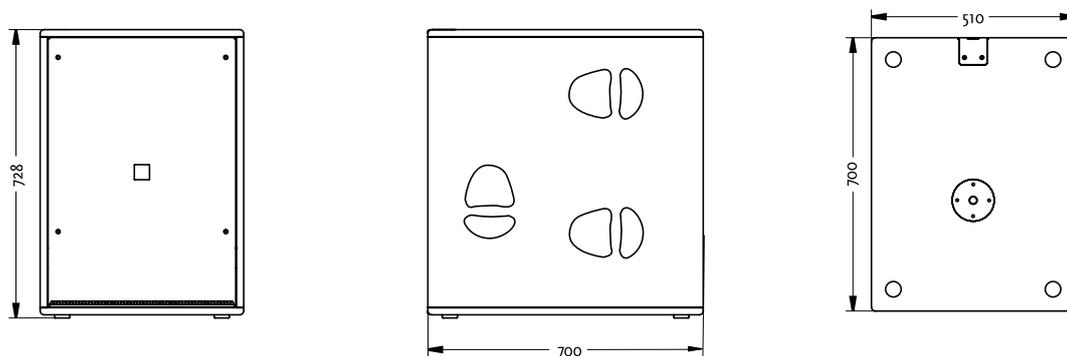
dimensions du coffrage du CTA 118 Sub en [mm]
